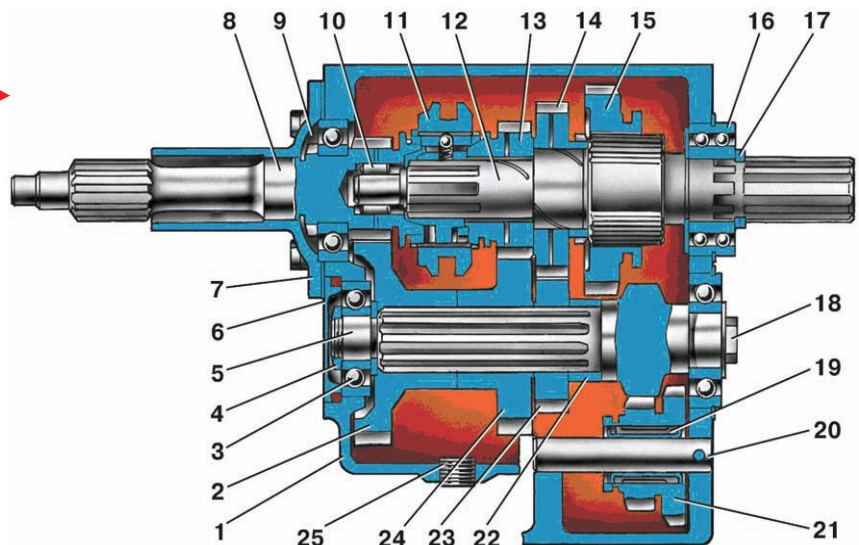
Коробка передач, синхронізована частково: 1 – картер; 2 – шестерня приво ду проміжн о ва лу; 3 – підшипник проміжн о ва лу; 4 – гайка; 5 – проміжний вал; 6 – кришка підшипника; 7 – передня кришка; 8 – первинний вал; 9 – спеціальна гайка; 10 – передній підшипник вторинн о ва лу; 11 – муфта синхронізатора; 12 – вторинний вал; 13 – шестерня III передачі; 14 – шестерня II передачі; 15 – шестерня I передачі; 16 – задній підшипник вторинн о ва лу; 17 – стопорні кільця; 18 – болт кріплення заднього підшипника проміжн о ва лу; 19 – підшипник блоку шестерень заднього ходу; 20 – вісь блоку шестерень заднього ходу; 21 – блок шестерень за днього ходу; 22 – втулка розпірна; 23 – шестерня II передачі проміжн о ва лу; 24 – шестерня III передачі проміжн о ва лу; 25 – пробка зливн о го отвору картера
